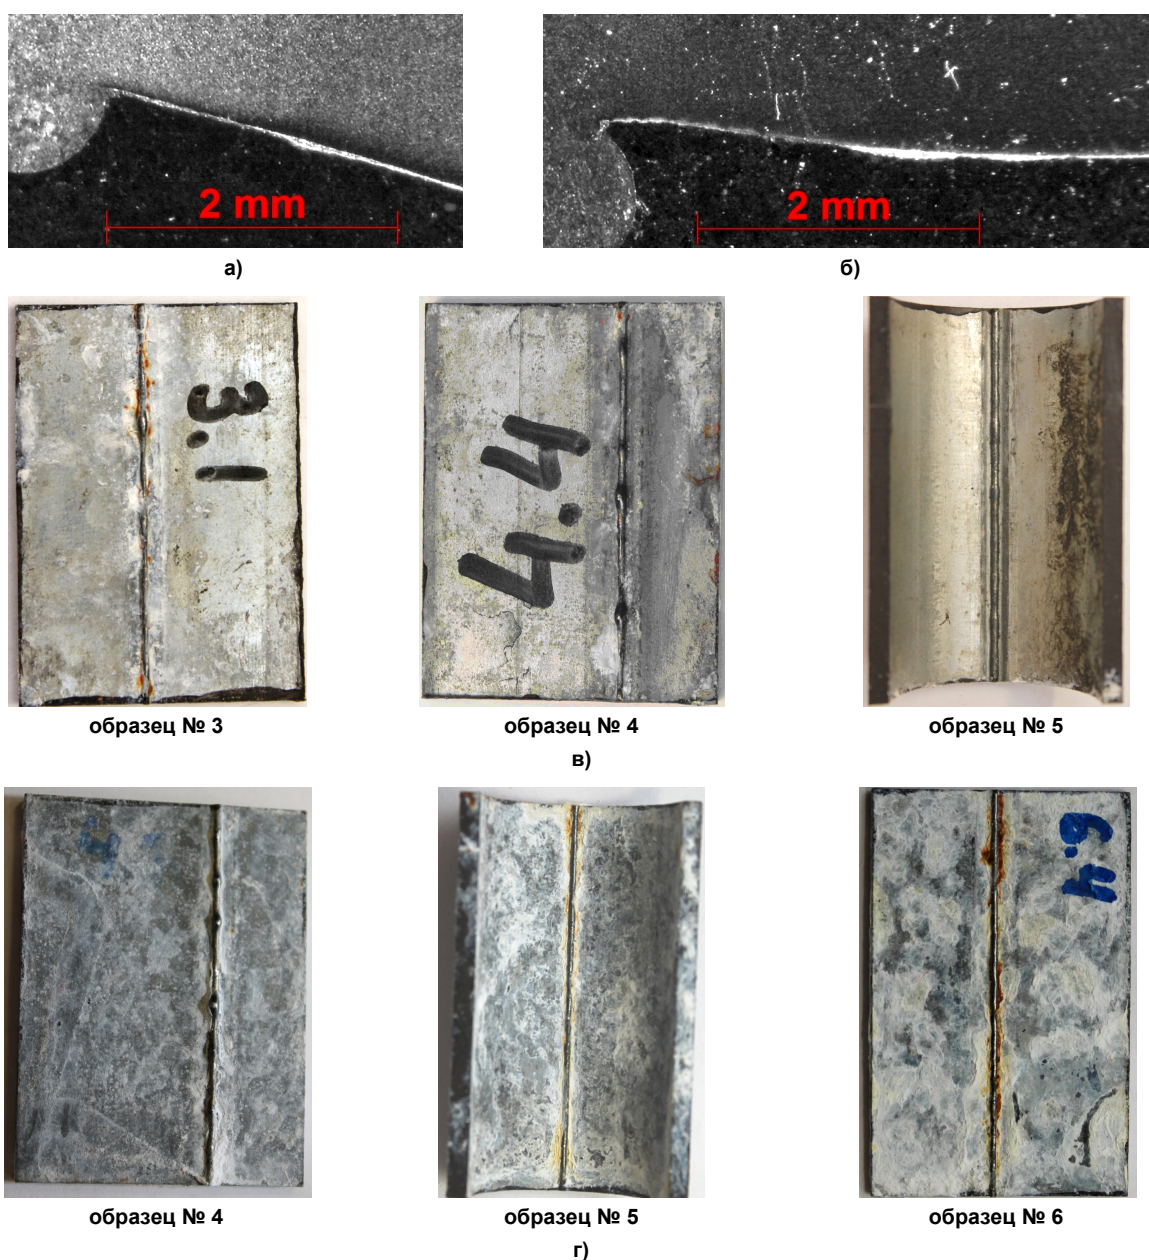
Виды сварного соединения отдельных образцов после коррозионных испытаний: а – вид поперечного шлифа зоны сварного соединения образца № 5; б – вид поперечного шлифа зоны сварного соединения образца № 3; в – образцы № 3, 4, 5 после коррозионных испытаний в камере при повышенных значениях относительной влажности воздуха и температуры с периодической конденсацией влаги; г – образцы № 4, 5, 6 после коррозионных испытаний в камере при воздействии нейтрального соляного тумана
